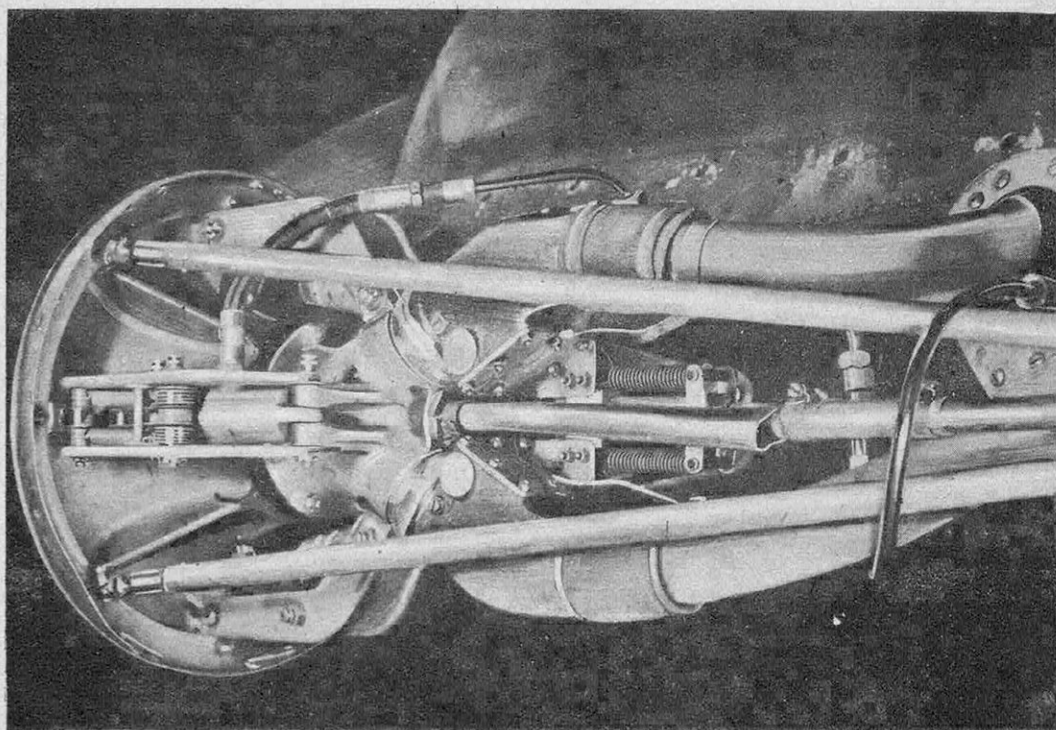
VUE ARRIÈRE DE L'ACCOUPLMENT PORTÉ PAR L'AVION RAVITAILLÉ
